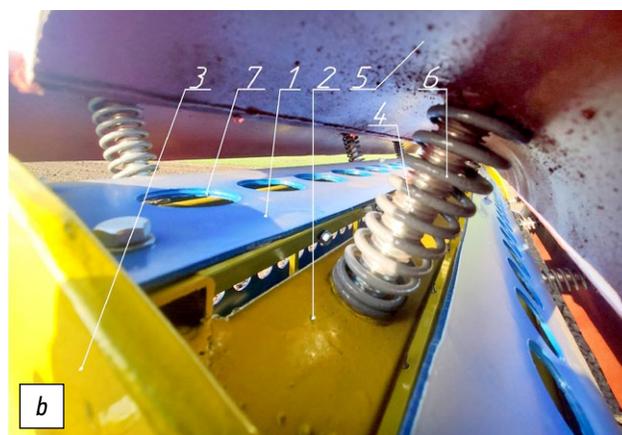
Пружинно-волновой каток: 1 — пластины образующей цилиндра; 2 — ребра; 3 — вертикальные диски; 4 — шпильки; 5 — уплотнители; 6 — пружины; 7 — отверстия.
